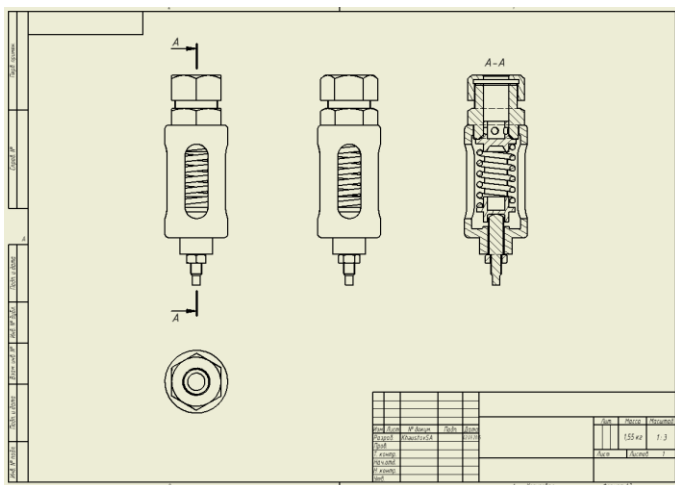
Сборочный чертеж предохранительного клапана
